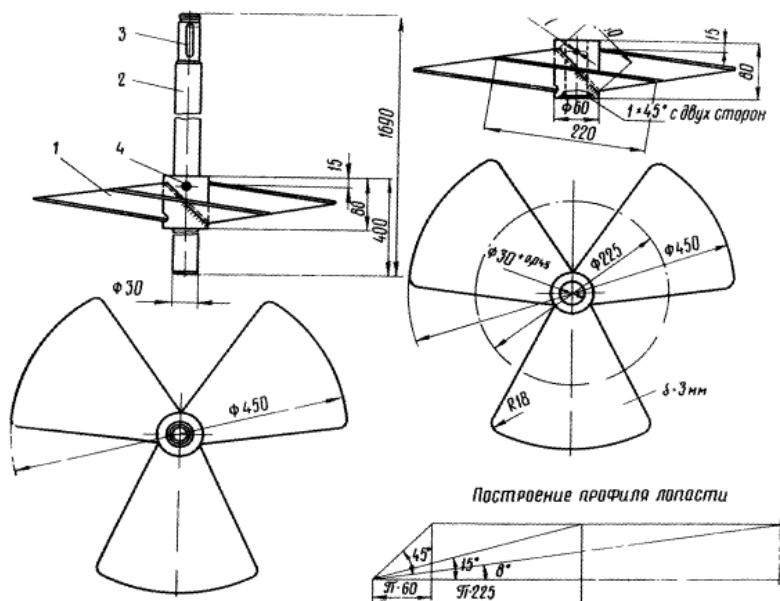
Вал смесителя с пропеллерной мешалкой:
